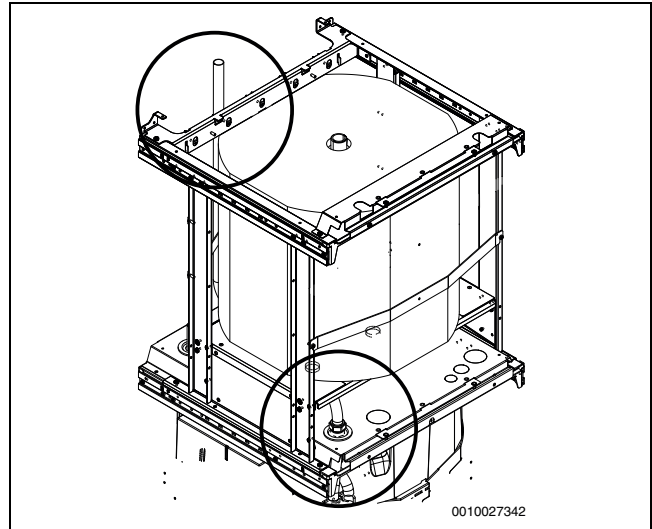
Montaggio di un tubo di raccordo nuovo (n. 11)
